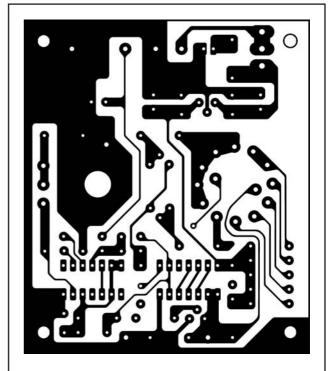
Dessin, à l'échelle 1, de la face "soudures" du circuit imprimé double face à trous métallisés du capacimètre pour multimètre.
